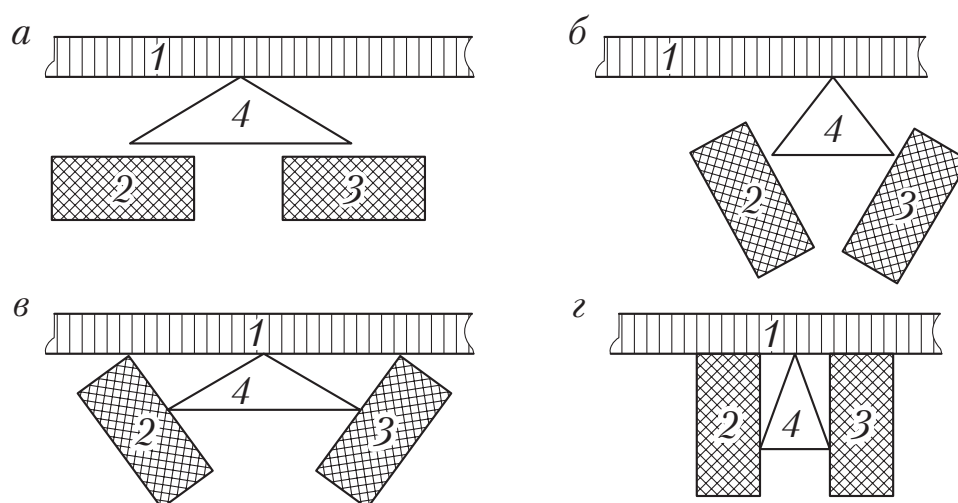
Варианты размещения станков при их обслуживании одним рабочим
